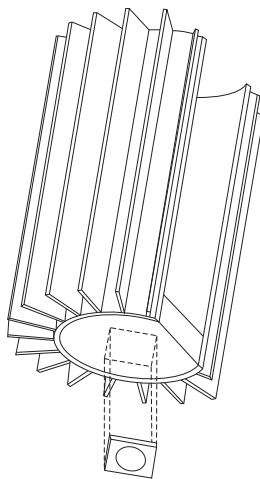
Корпус радиатора с вертикальными ребрами и полый внутри
